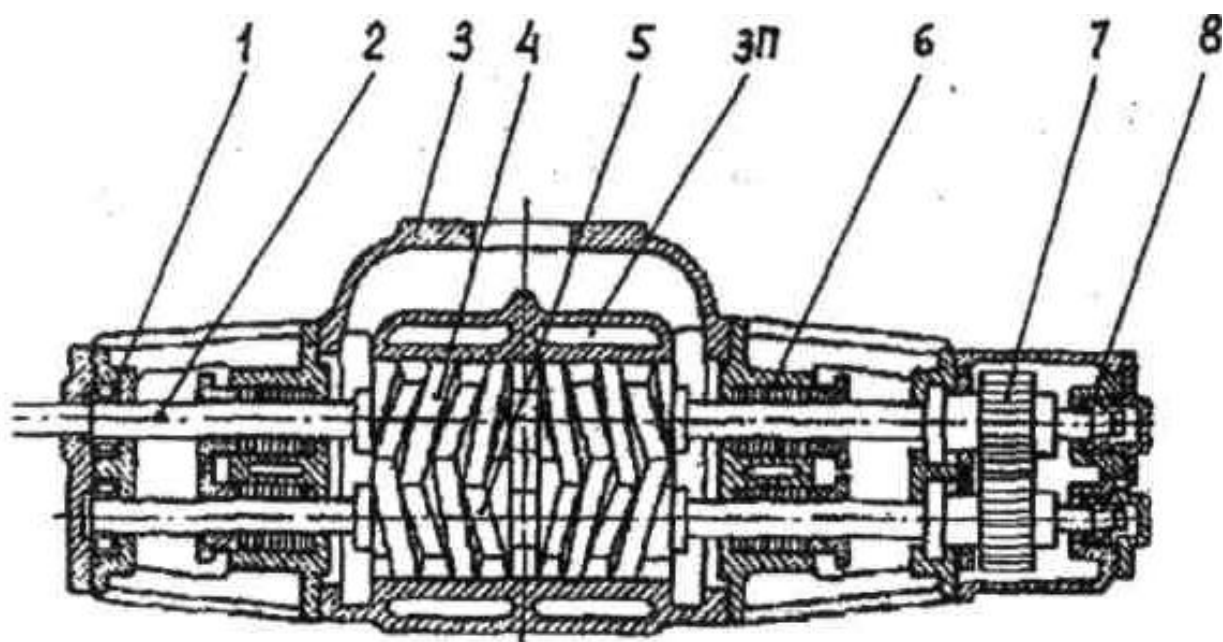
Двухвинтовой насос: 1,8 - подшипники; 2 - приводной вал, 3 - корпус; 4,5 - винты; 6 - сальниковое уплотнение вала; 7 - синхронизирующие шестерни; ЗП - зарубашечное пространство
